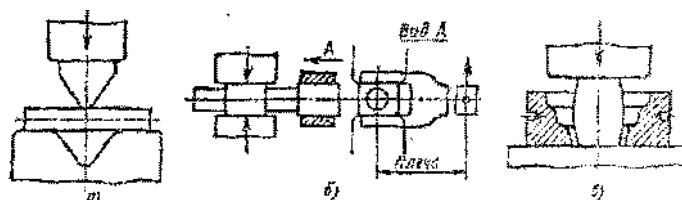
Схемы: а - гибки; б - скручивания; в - штамповки в подкладном штампе
